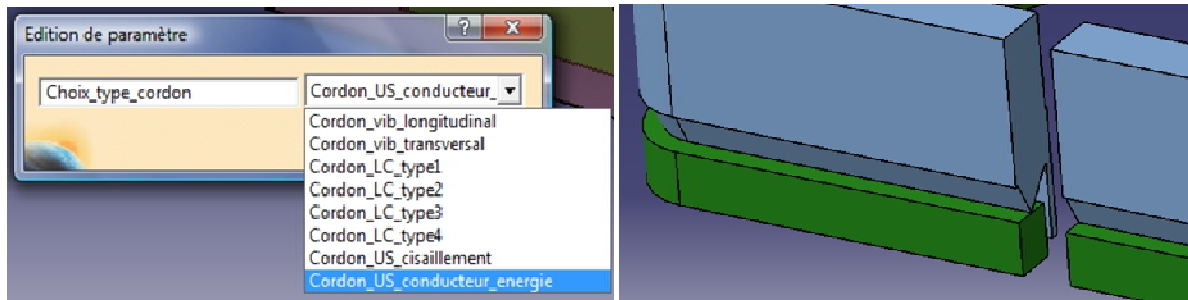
Même profil que sur la figure 95, avec un type de soudure par ultrasons.
